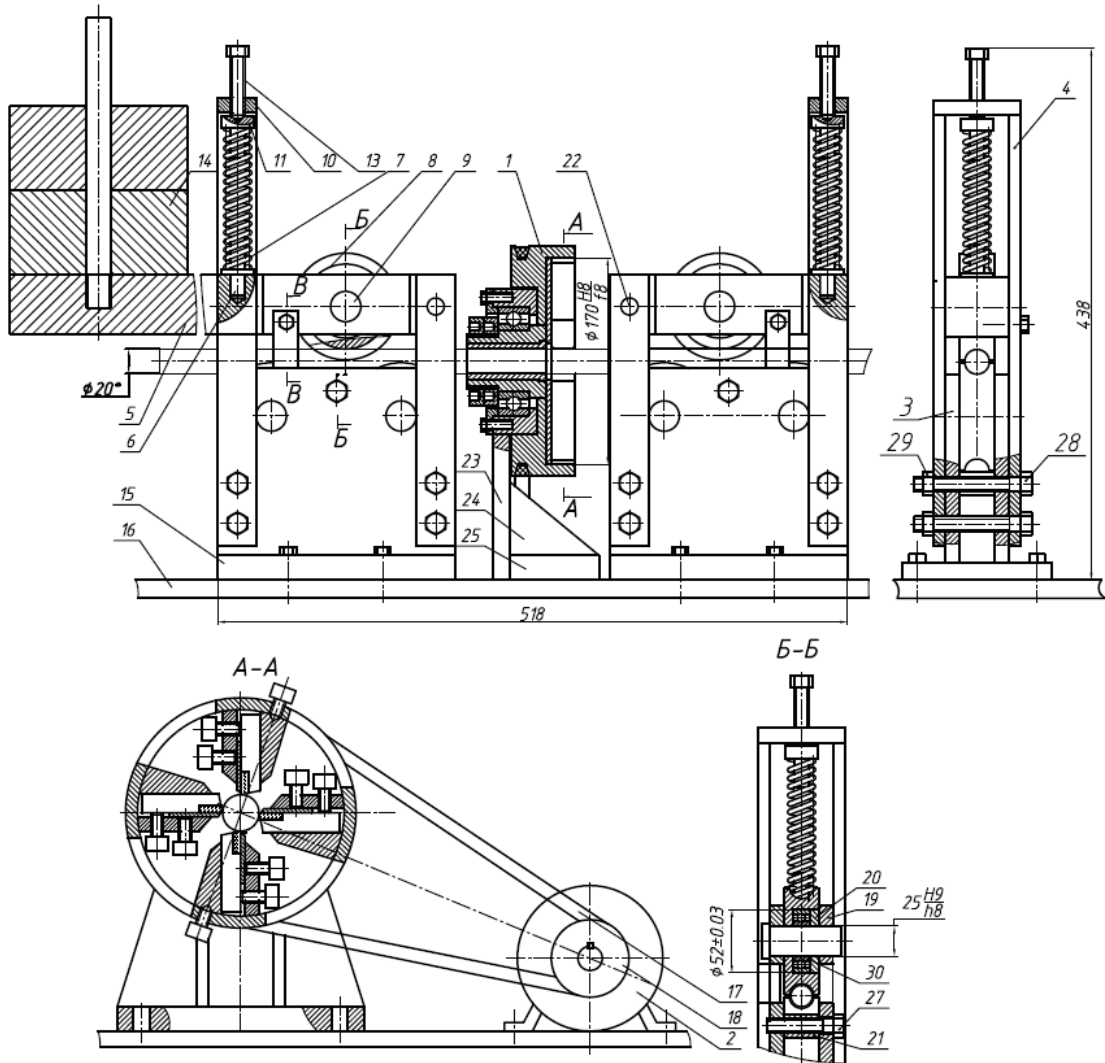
Чертеж устройства для обтачивания длинных валов.
